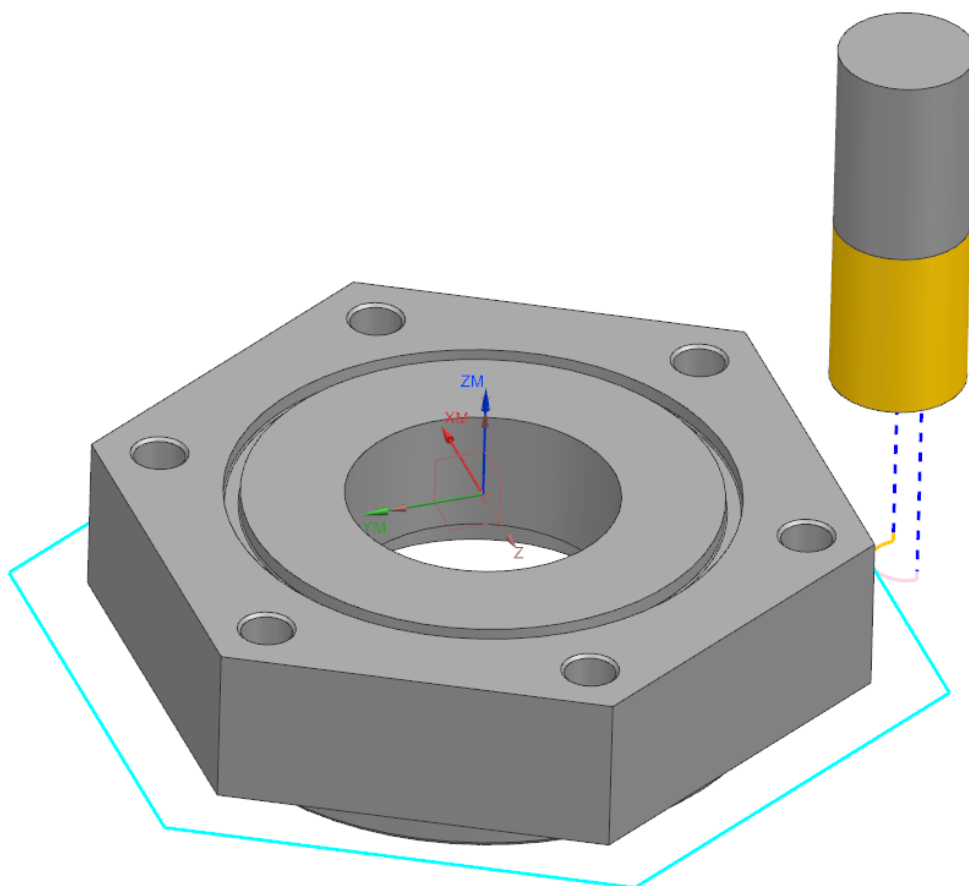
Створення траєкторії руху інструмента при фрезеруванні
